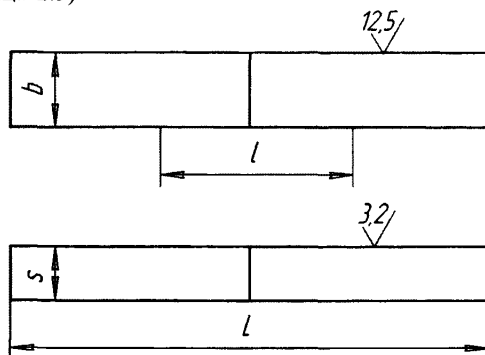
Образец для испытания сварного соединения на статический изгиб
